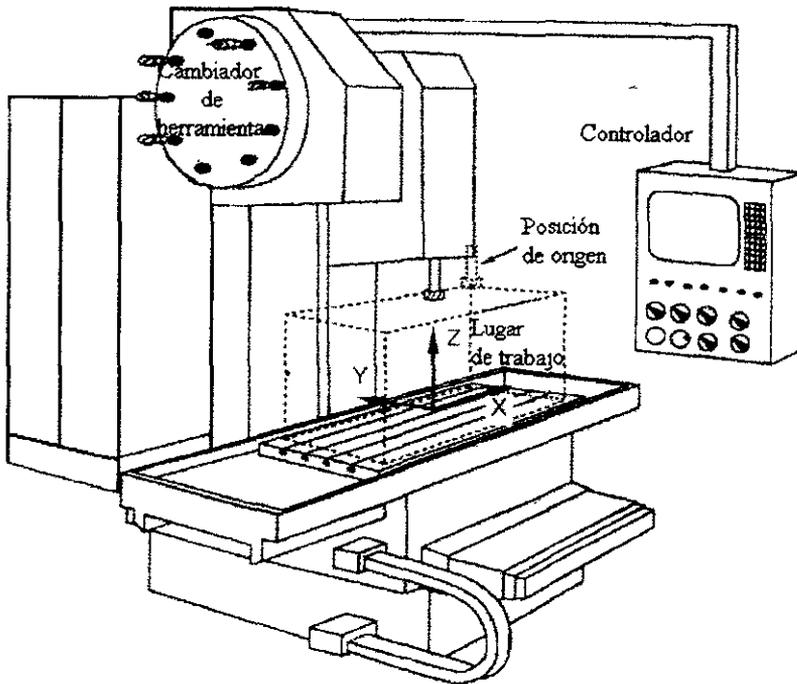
Componentes principales de una máquina fresadora de CNC.
